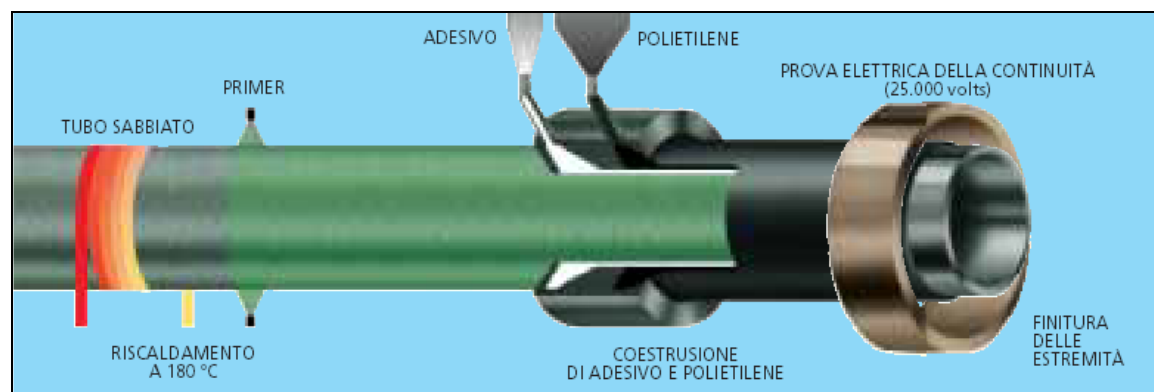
Struttura di un tubo di acciaio di tab. 3.I, protetto all'esterno e l'interno.
